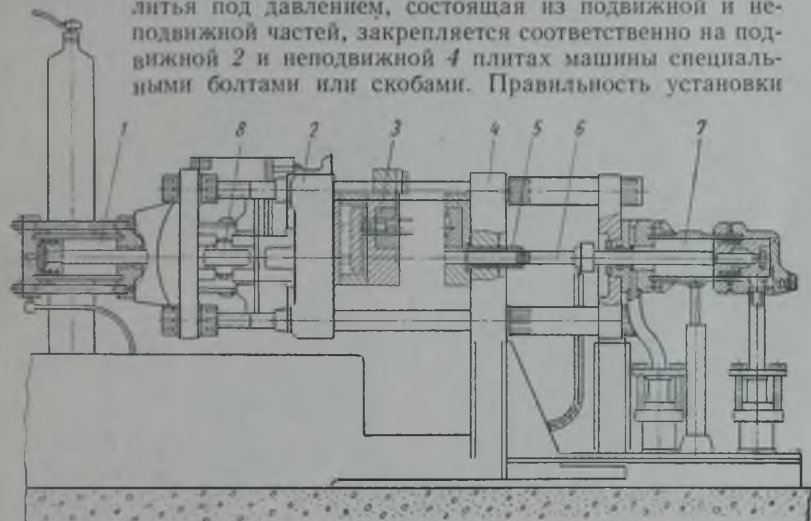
Схема машины для литья под давлением с горизонтальной холодной камерой прессования
